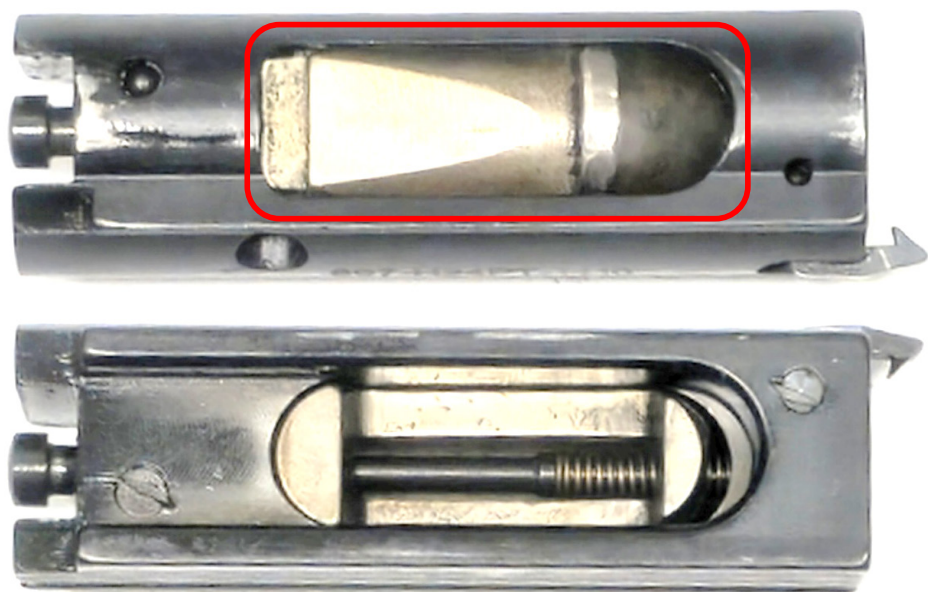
Zespół przesuwny – widok z góry, zaznaczona ramka suwadła
